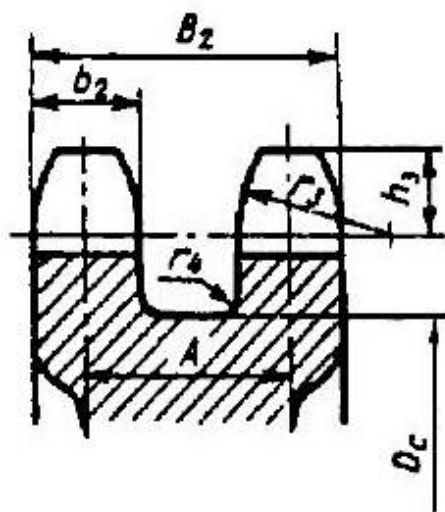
Размеры зуба и венца звездочки в поперечном сечении
